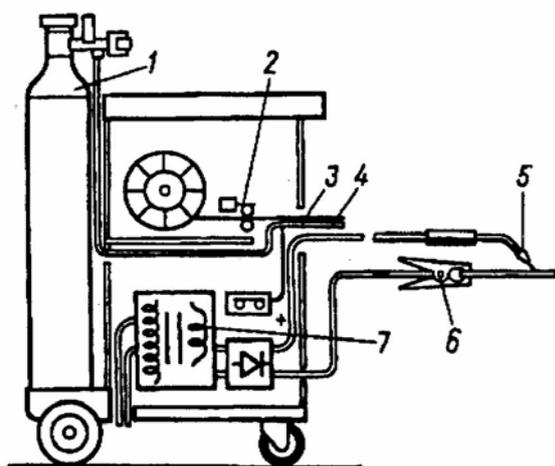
Схема полуавтомата для сварки в среде защитных газов: 1 – баллон с углекислым газом; 2 – механизм подачи проволоки; 3 – проволока; 4 – трубопровод подачи газа; 5 – горелка; 6 – заземление; 7 – трансформатор
